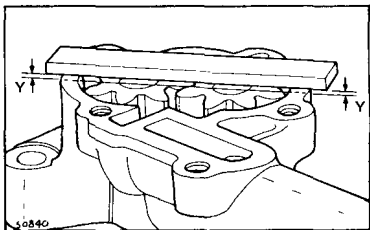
Проверьте зазор между торцами шестерен и внутренней поверхностью крышки
